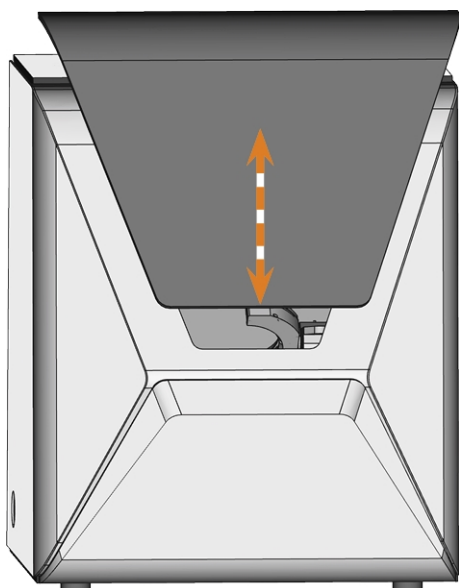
OUVRIR ET FERMER LA PORTE DU LOCAL DE TRAVAIL
